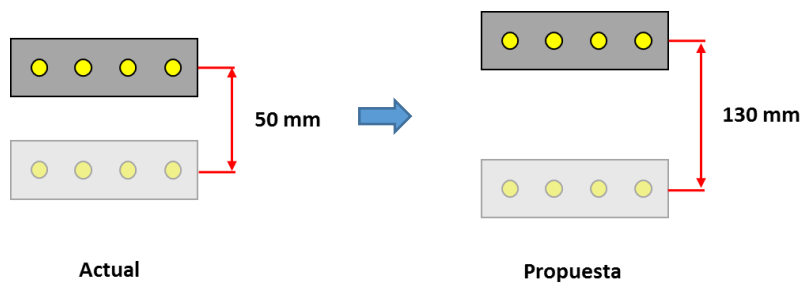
Alternativa 3: retrofitting de la placa caliente
